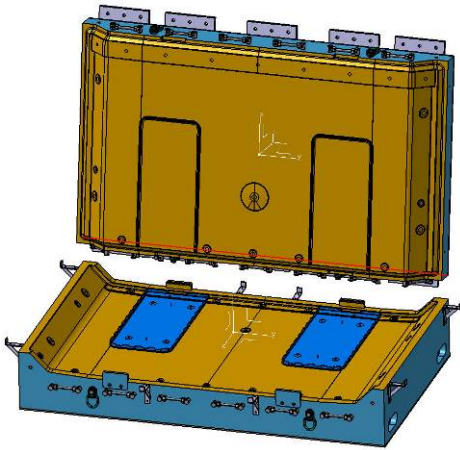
Werkzeug Bodenplatte 1 (CAD)
